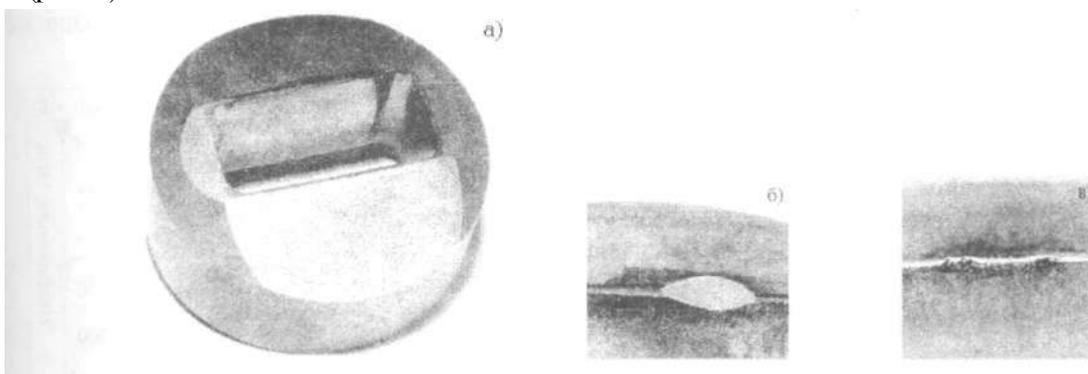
Обсечный пуансон а) внешний вид; б) характер усталостного разрушения режущей кромки; в) износ рабочей поверхности.
